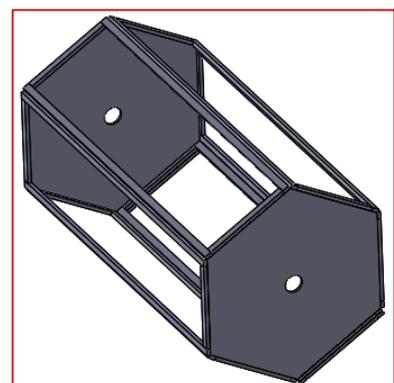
Croquis del "esqueleto" del tambor hexagonal
